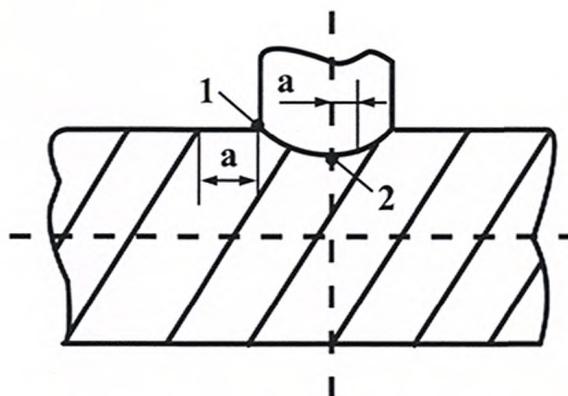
Сварка патрубков (штуцеров) с трубопроводами со спиральными швами
